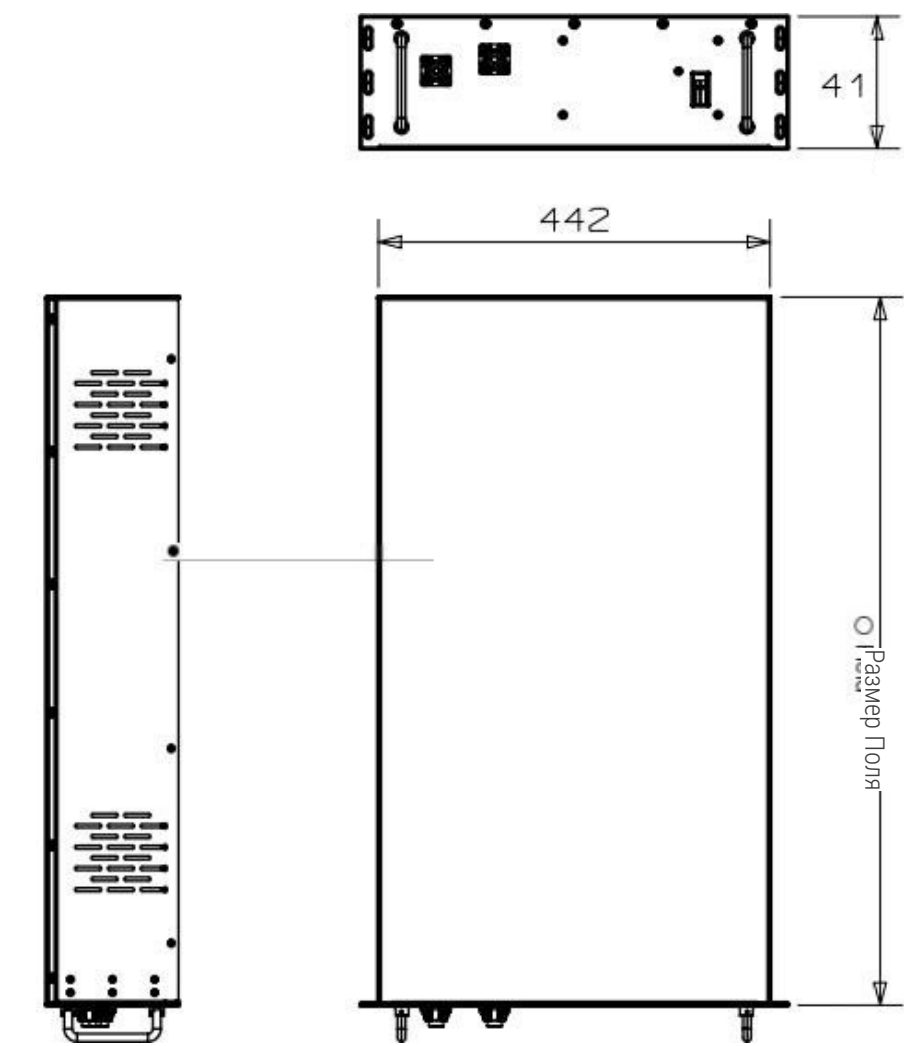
Внешний вид и монтажно-габаритная схема модуля
